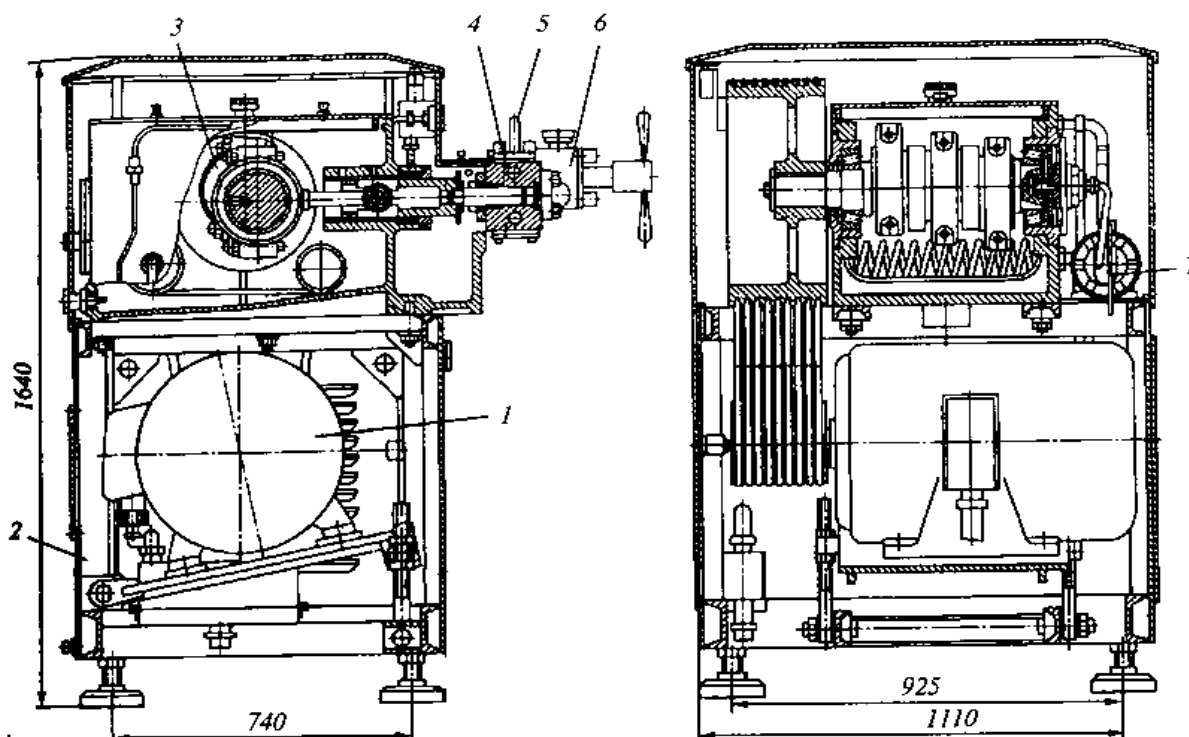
Общий вид гомогенизатора марки К5-0ГА-1,2:
